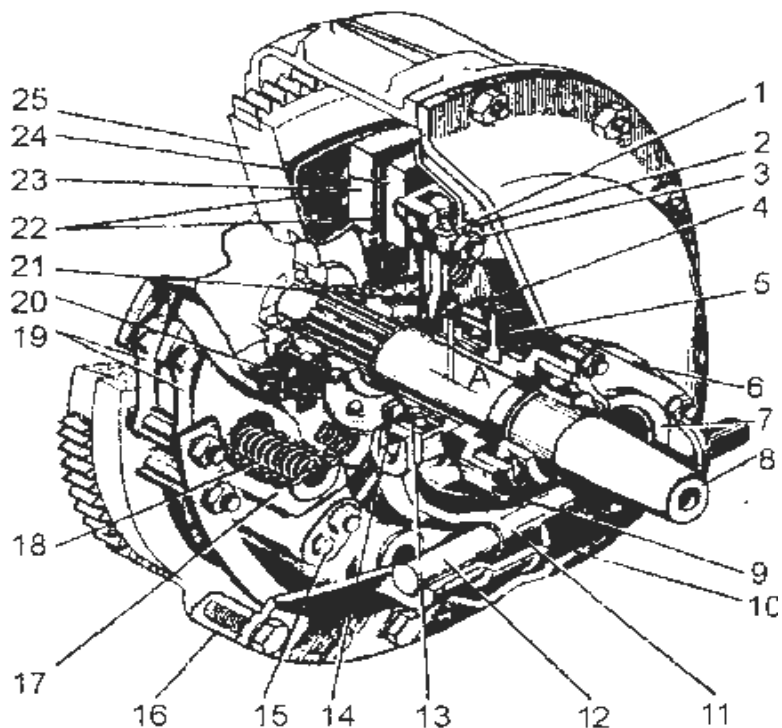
Муфта сцепления дизелей Д-442: 1 – вилка; 2 – шайба стопорная; 3 – гайка регулировочная; 4, 6 – масленки; 5 – корпус муфты выключения; 7 – крышка сальника; 8 – вал сцепления; 9 – корпус наружного подшипника; 10 – крышка муфты сцепления; 11 – вилка выключения; 12 – валик вилки выключения; 13 – упор нажимного подшипника; 14 – кольцо отжимное; 15 – болт; 16 – картер маховика; 17 – кожух; 18 – пружины; 19 – пакеты ведущих пластин; 20 – гаситель крутильных колебаний; 21 – рычаг отжимной; 22 – диски ведомые с фрикционными накладками; 23 – диск промежуточный; 24 – диск нажимной; 25 – маховик: а – зазор 3,5–4,5 мм
